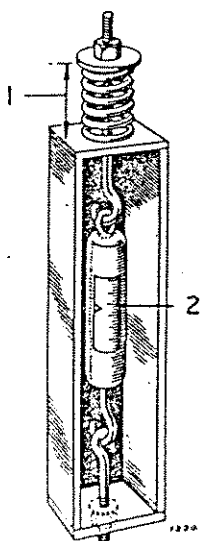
Spannringe für Zylinderlaufbuchsen, (Spezial-)Werkzeug Nr. S.138
